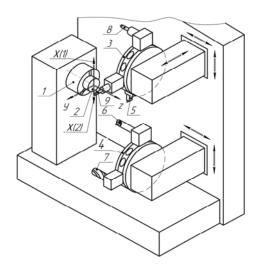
Структурная схема станка с двумя револьверными головками: I – шпиндель; 2 – деталь; 3 – РГ1; 4 – РГ2; 5 – резец в РГ1; 6 – резец в РГ2; 7 – сверло в РГ2; 8, 9 – приводные блоки с инструментами
